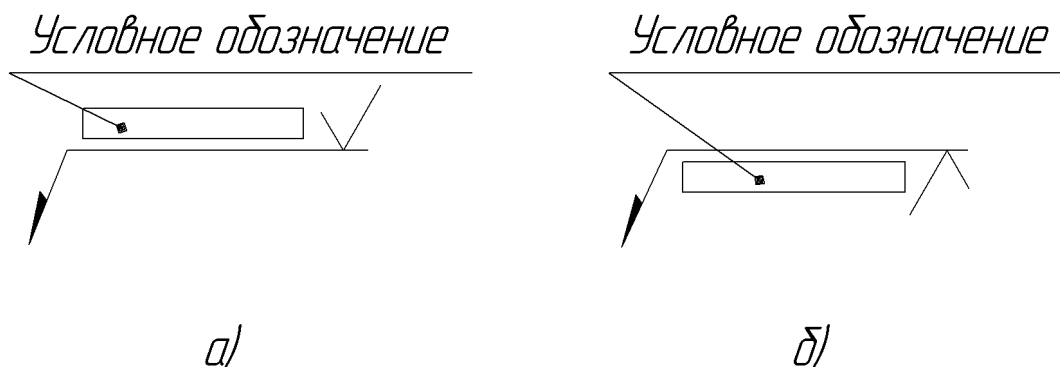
Обозначение шероховатости механически обратной поверхности шва: а) с лицевой стороны; б) с оборотной стороны
